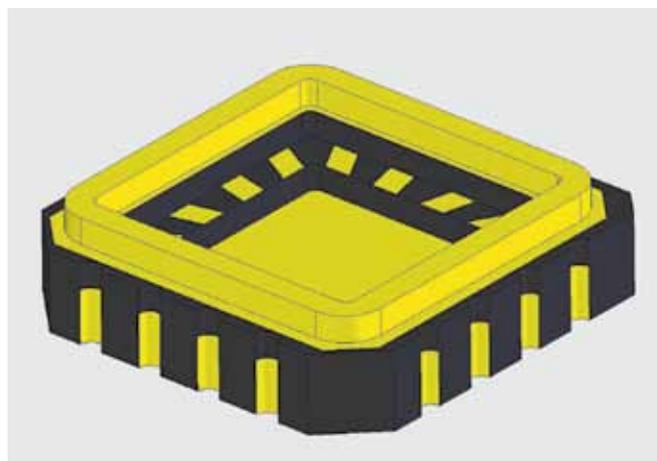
Металлокерамический корпус типа CLCC с 16-выводными площадками
